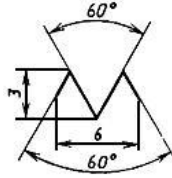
Обозначение рельефа рабочих поверхностей.
